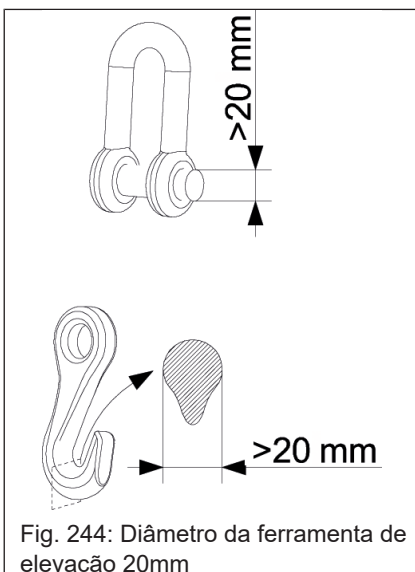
Diâmetro da ferramenta de elevação 20mm
